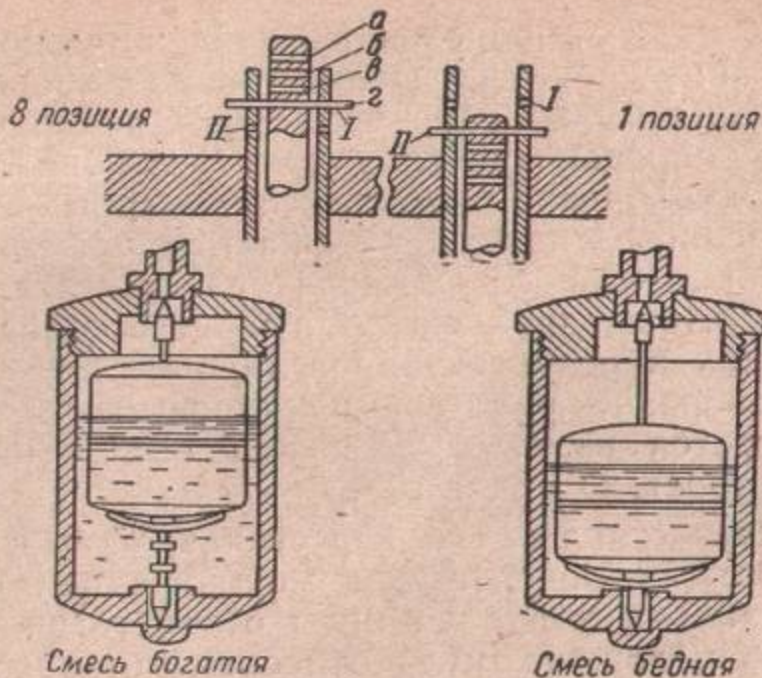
Регулировка карбюратора перестановкой иглы поплавка и иглой дросселя¹
